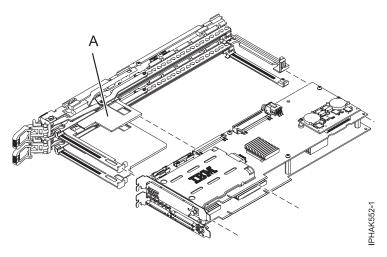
Installation de la carte double largeur dans le bloc-cassette.
